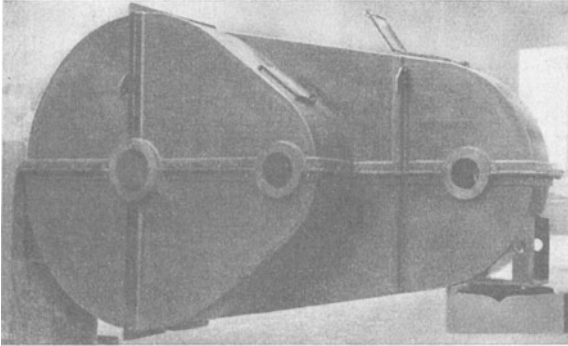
Großer geschweißter Radschutzkasten.
